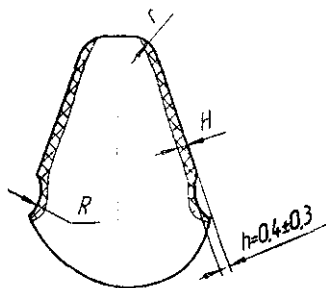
Профиль зуба шлифуемого зубчатого колеса
